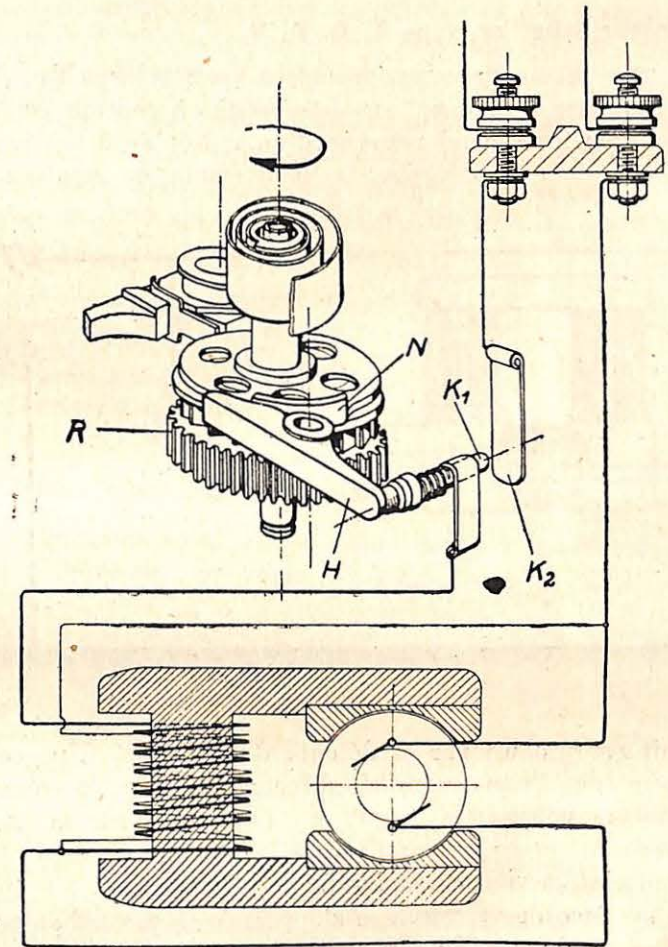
Exploseur Schaffler type A. B. F. V.
